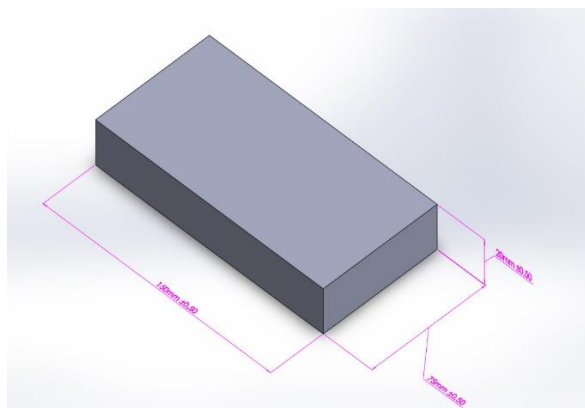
Molde hecho en Solidworks de la probeta para prueba de flexión.
